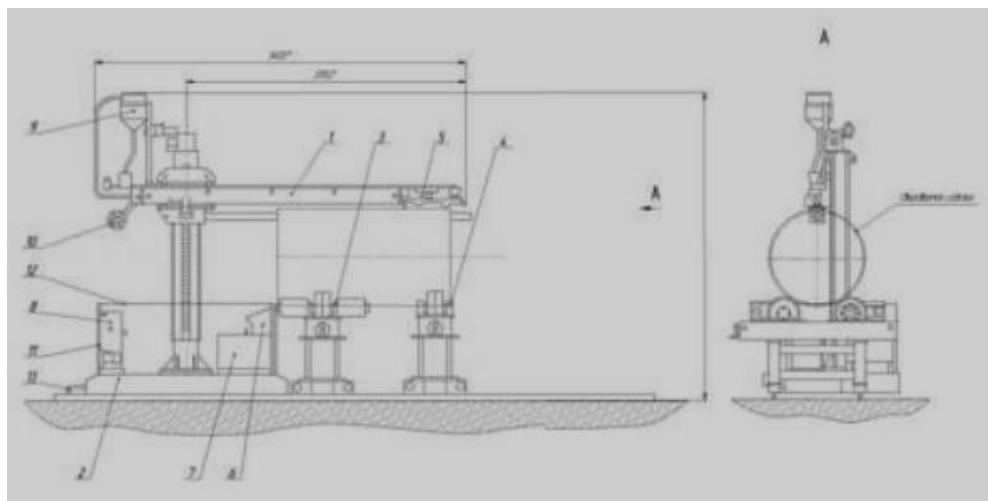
Схема установки для зварювання корпусу контейнера
